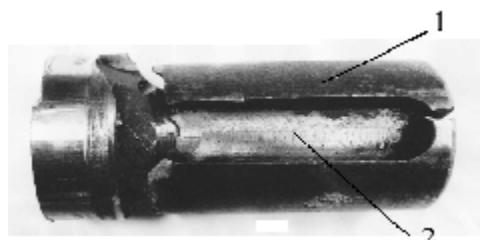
Поверхня шпонкового паза після механічного оброблення:
